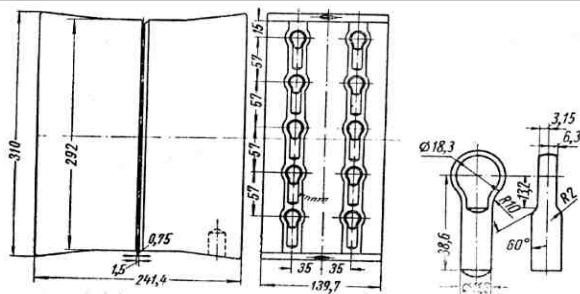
Ручьевая вставка для многоручьевой штамповки в один переход и чертеж типовой горячей поковки [6]
